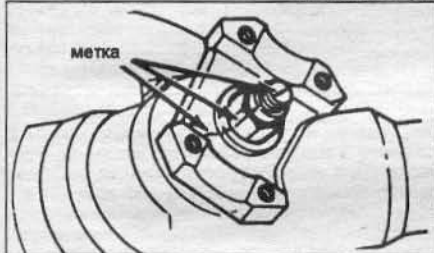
Нанесение меток относительного положения деталей крепления фланца к шестерне главной передачи.
